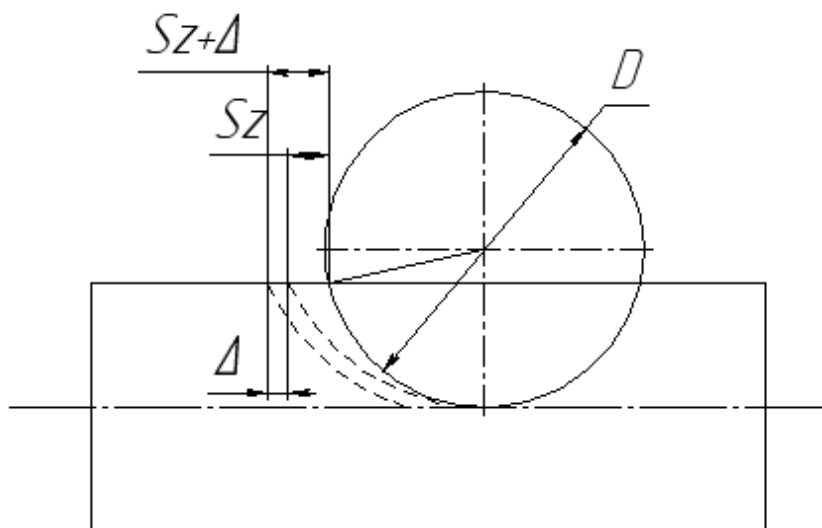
Схема несимметричного торцового фрезерования
